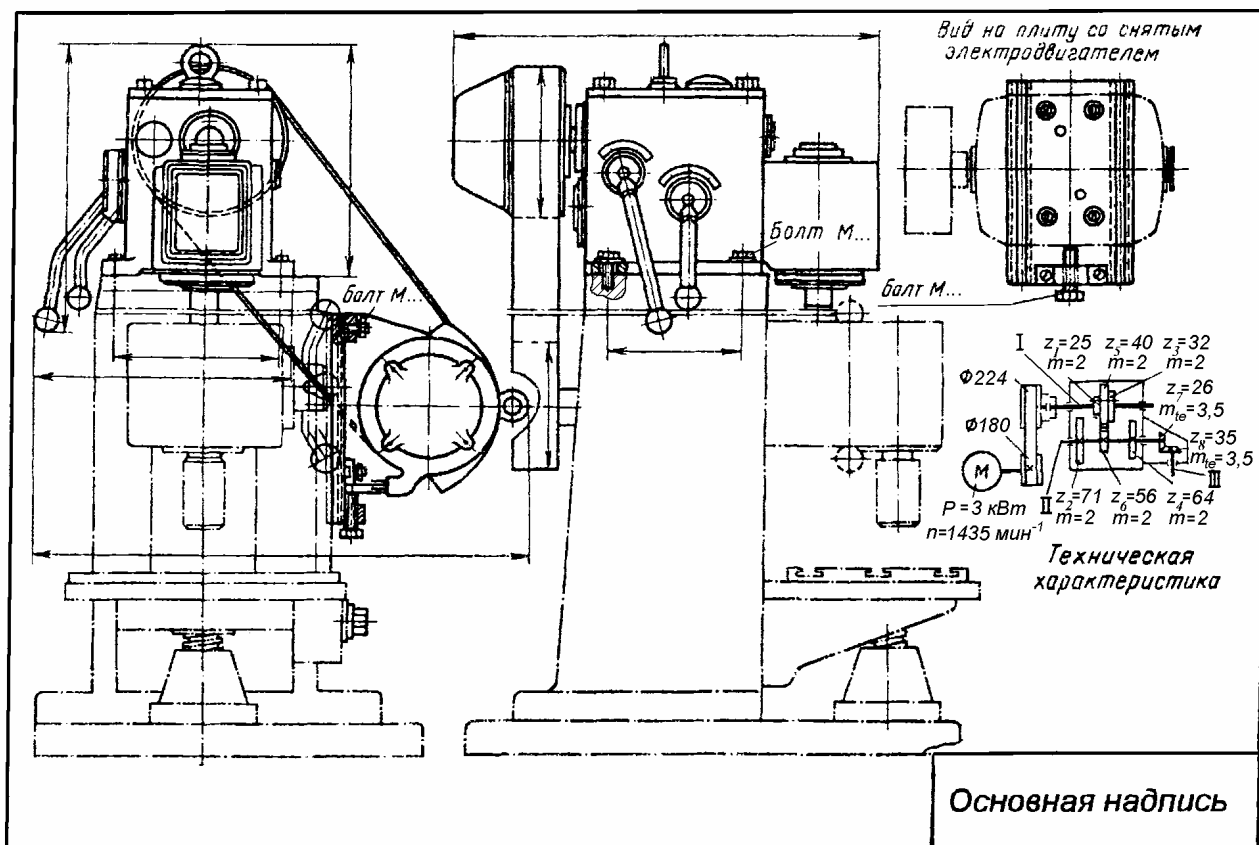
Общий вид привода фрезерного станка с установкой на станине
